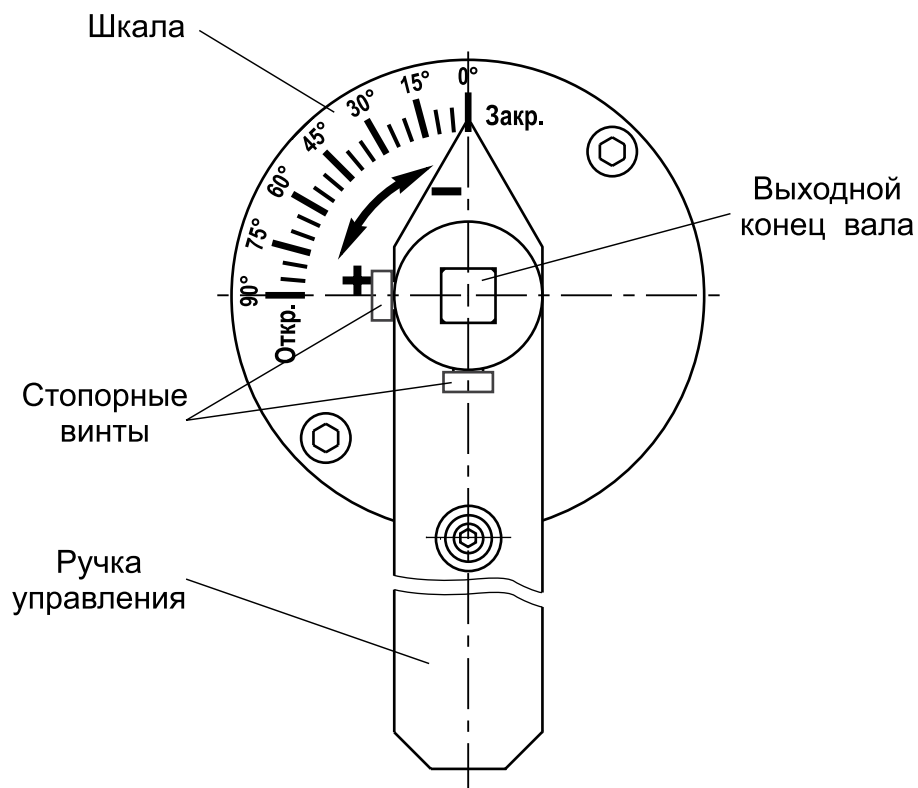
Заслонки дроссельные с ручным управлением (вид сверху)
